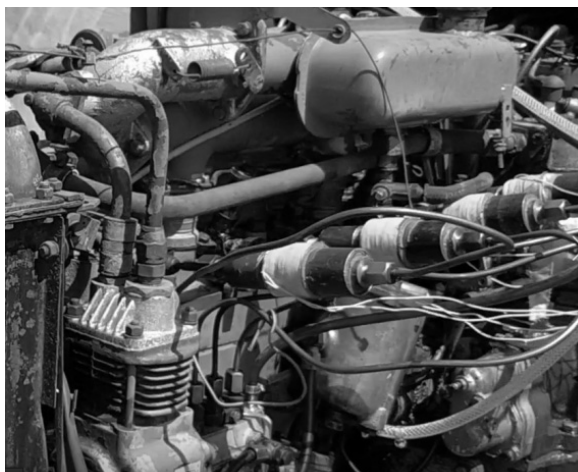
Фрагмент монтажа устройств для магнитной обработки топлива на форсунки двигателя Д-240 трактора МТЗ-80
